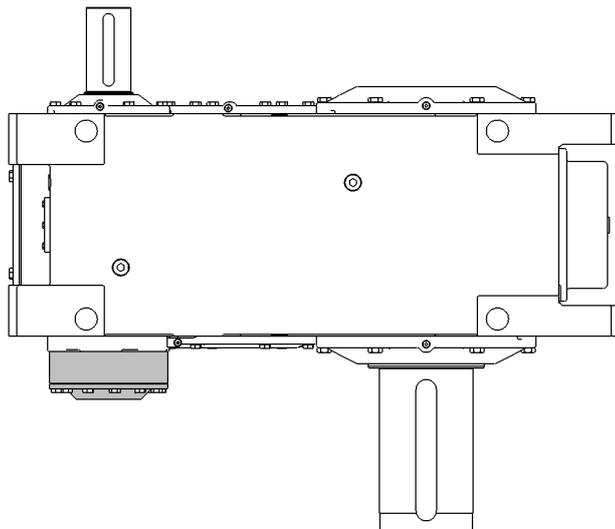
Промышленный редуктор с блокировкой обратного хода (принципиальная схема)
